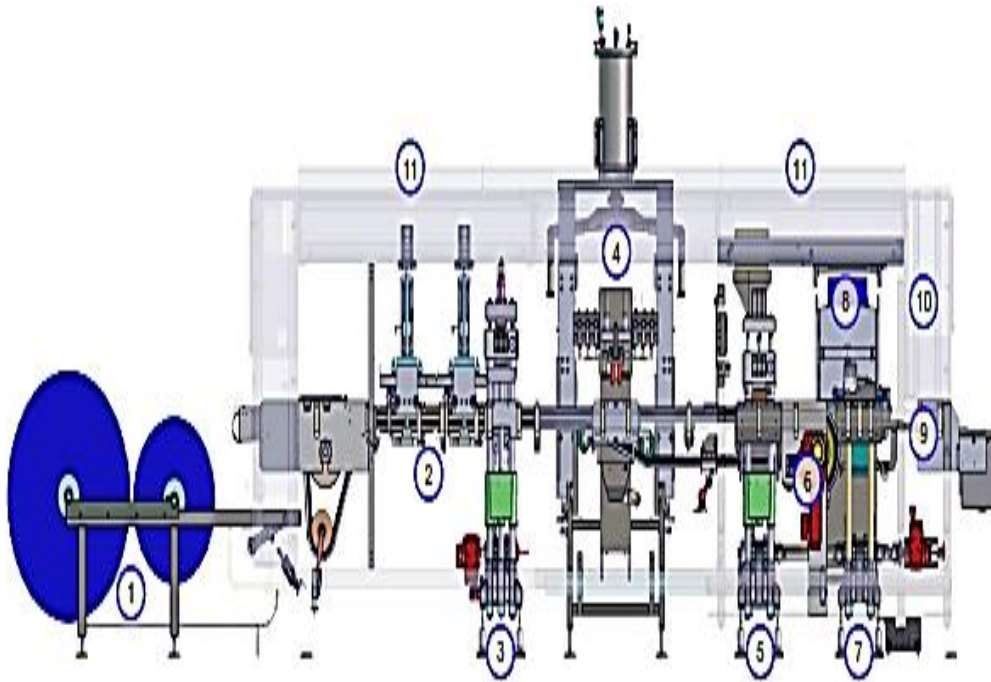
Schéma d'ensemble de la machine ERCA MF 21[30]
